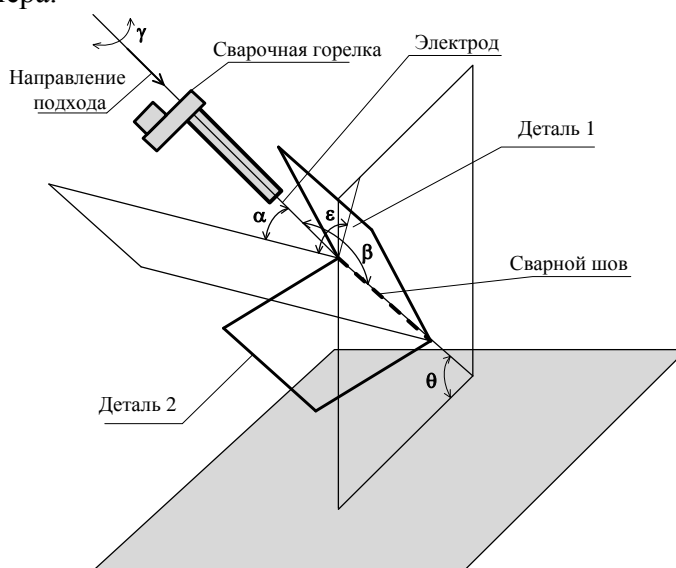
Ориентация горелки дуговой сварки и сварного шва
